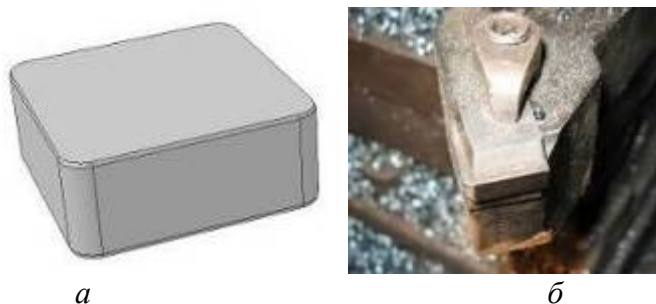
Схематическое изображение режущей пластины формы SNGN 120412 (а) и внешний вид крепления пластины к державке (б)
